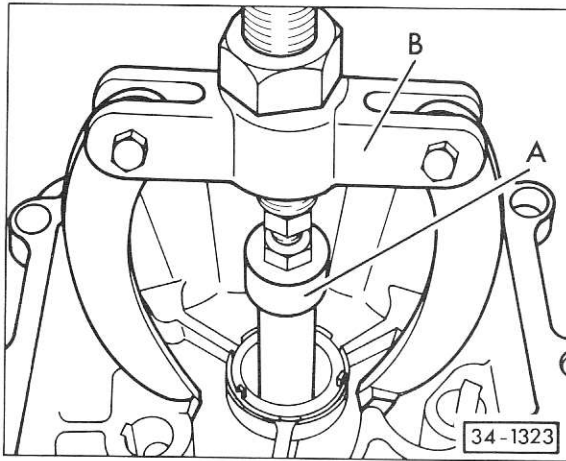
Roulement: extraction du couvercle du bouclier-support
